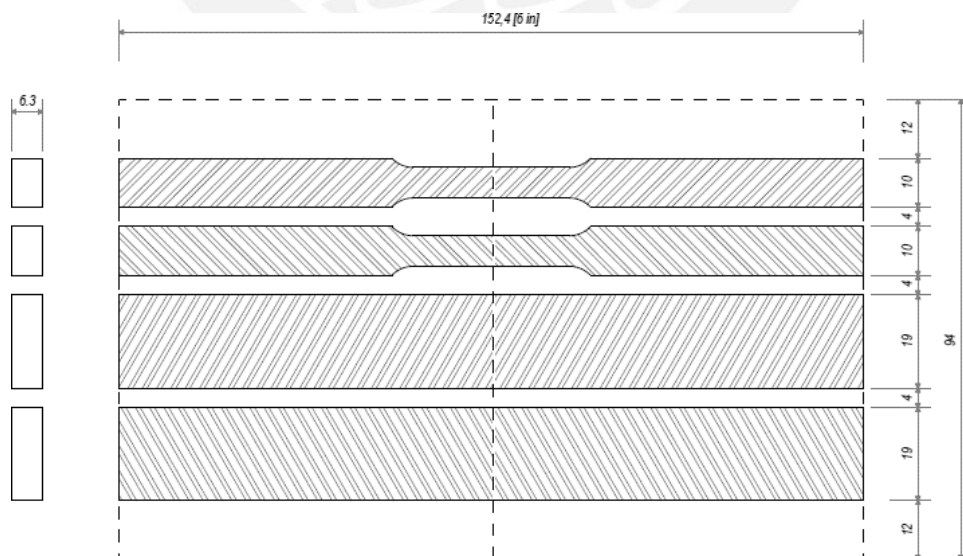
Distribución de cupón de soldadura formado por dos laminas soldadas de espesor variante de 6.2 mm- 6.3 mm. Ancho 94 mm y largo 76 mm
